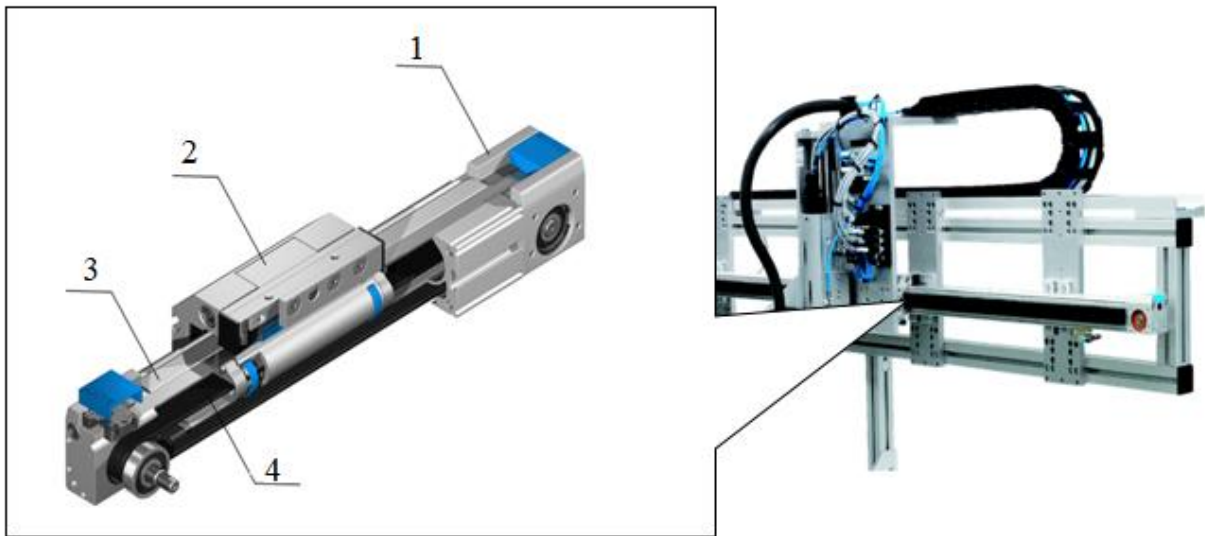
«Ось» із зубчато - пасовою передачею: 1 – корпус, 2 – напрямна, 3 – каретка, 4 – зубчато-пасова передача
